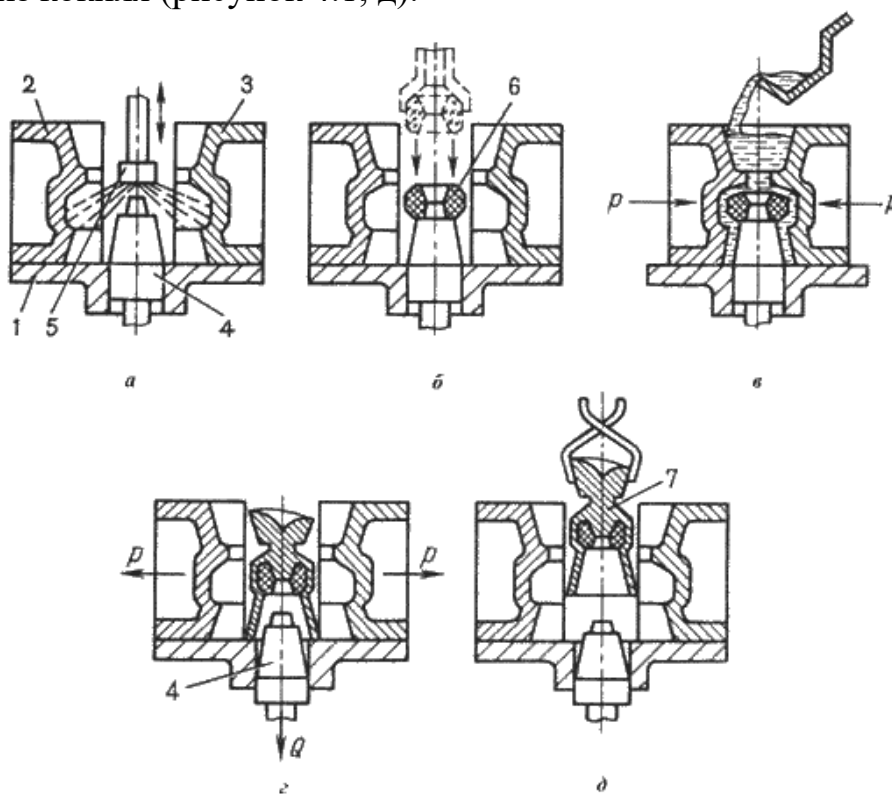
Технологические операции изготовления отливки в кокиль
